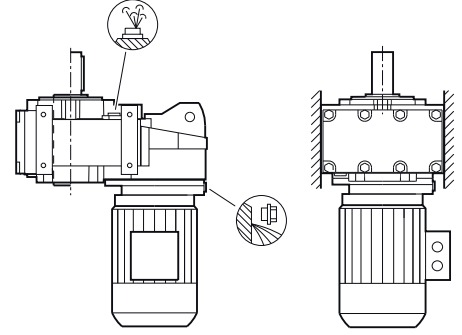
Yassı dişli için montaj konumları F.F Flanşlı model ve gövde flanşlı F.Z, Boyutlar 39 - 89
